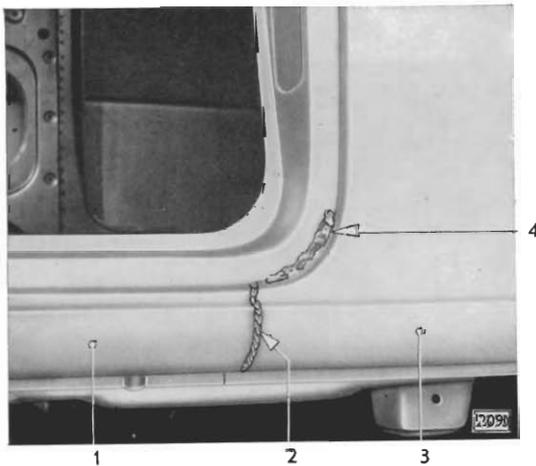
Stoßfuge zwischen neuer Seitenwand und Einstiegverkleidung autogen zugeschweißt und Seitenwand am Radenauslauf hartgelötet
